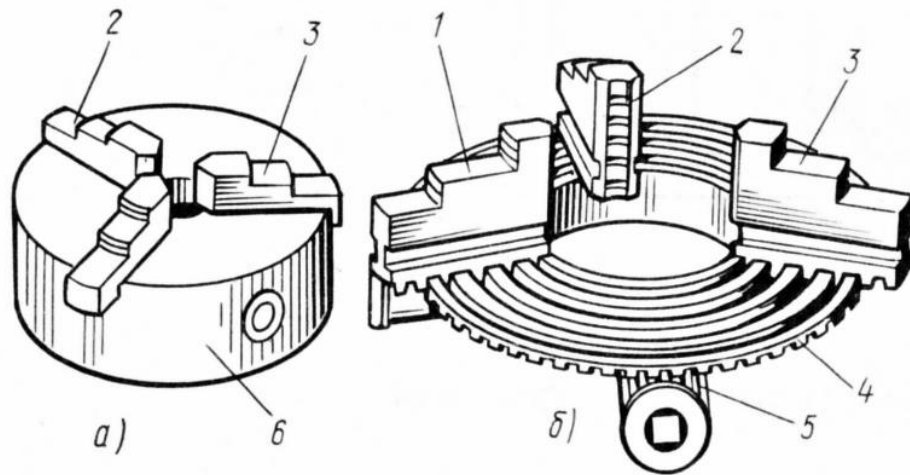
Трехкулачковый патрон с архимедовой спиралью: 1, 2 и 3 – кулачки; 4 – диск с с круговой рейкой по архимедовой спирали; 5 – приводная шестерня; 6 - корпус
